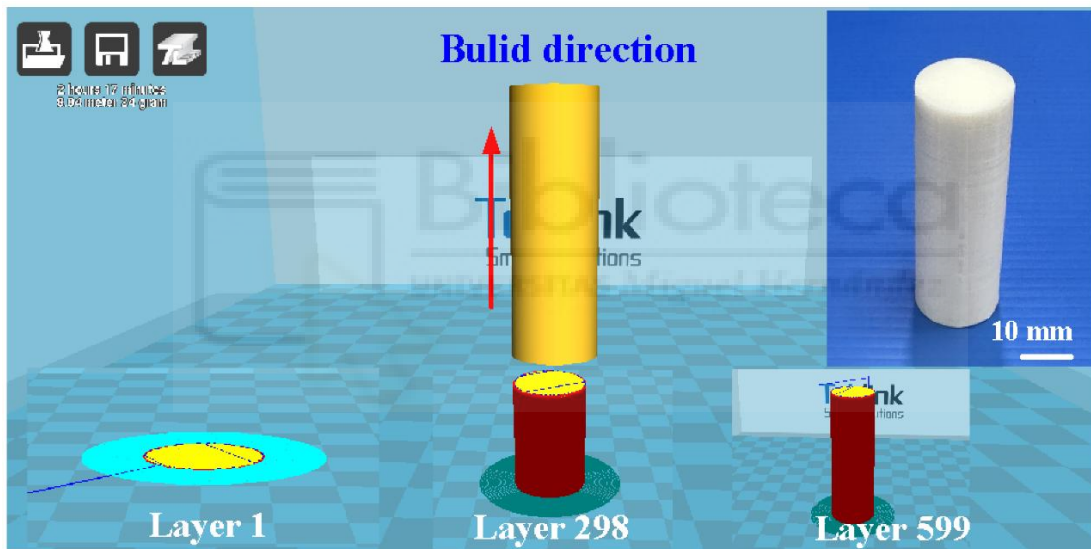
Probetas cilíndricas previas al proceso de soldadura por fricción [21].
